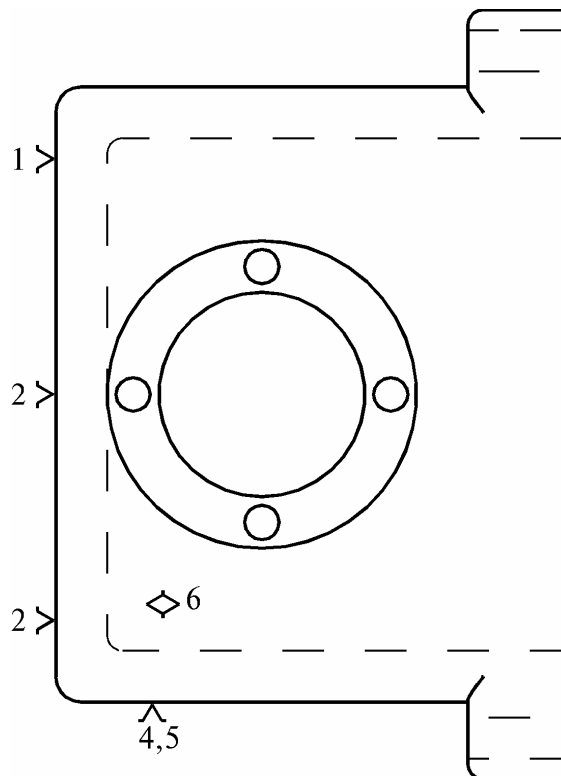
Схема базирования корпуса при обработке на многоцелевом станке
